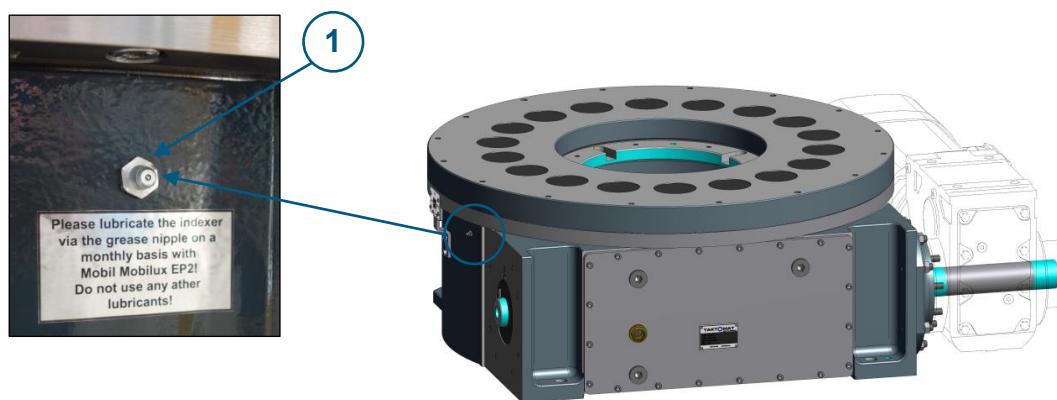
Смазка делительно-поворотных столов типов TMF2000 - TMF8000
